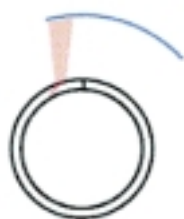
Schweißnahtprüfung am Rohr mit Array-Technik
